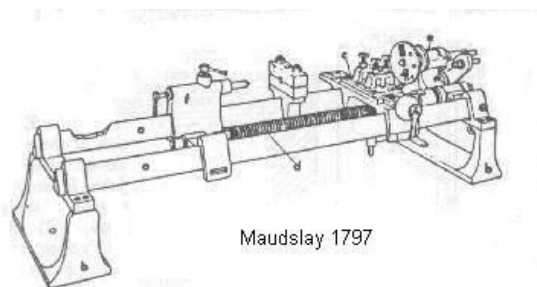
Перший токарно-гвинторізний верстат Модслі, [39].
